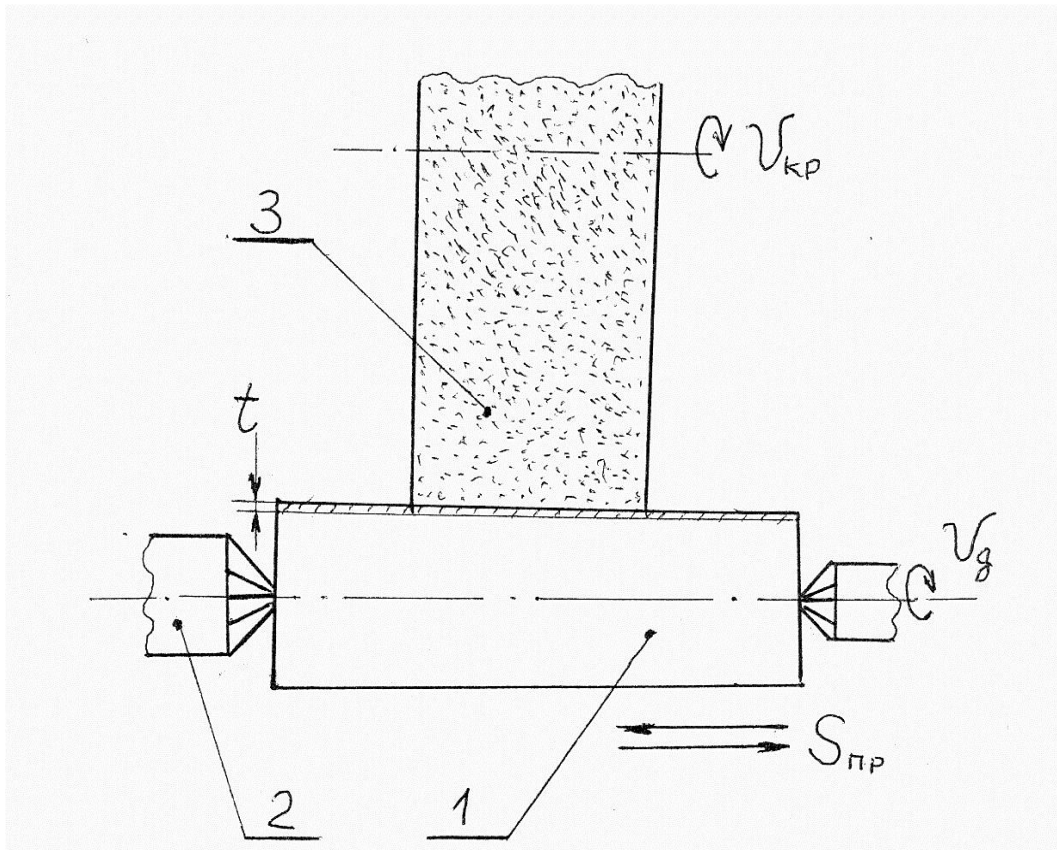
Спосіб тонкого кубонітового оброблення циліндричних поверхонь зносостійких деталей обертання з композиційних сплавів на основі нікелю для друкарських машин
